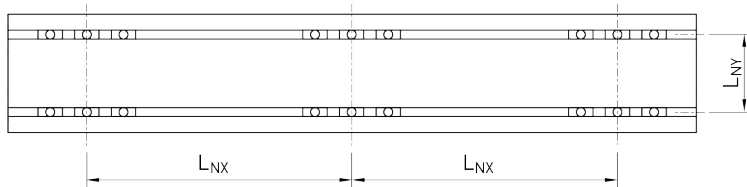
Befestigung mit Nutensteinen – HT250L, HB250L
